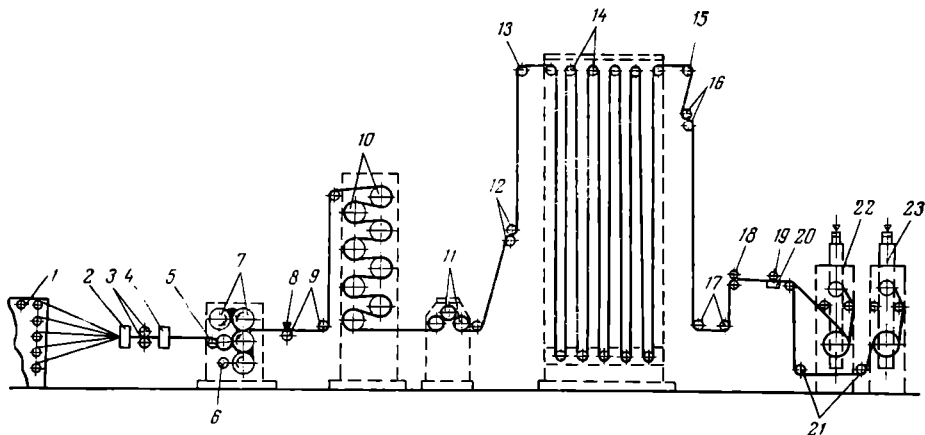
Схема обрезинивания металлического корда на поточной линии ЛОМК-800-К: 1 — шпулярник; 2 — нитесборник; 3, 9, 13, 15, 17, 21 — направляющие ролики; 4 — распределительная гребенка; 5 — шаговый валик с канавками; 6 — поддерживающий ролик; 7 — каландр; 8 — кромочные ножи; 10 — барабаны холодильной установки; 11 — натяжная станция; 12, 16 — центрирующие устройства; 14 — компенсатор; 18 — прижимно-натяжной валик; 19 — дисковый нож отрезного станка; 20 — плоский нож отрезного станка; 22, 23 — закаточные станки.
